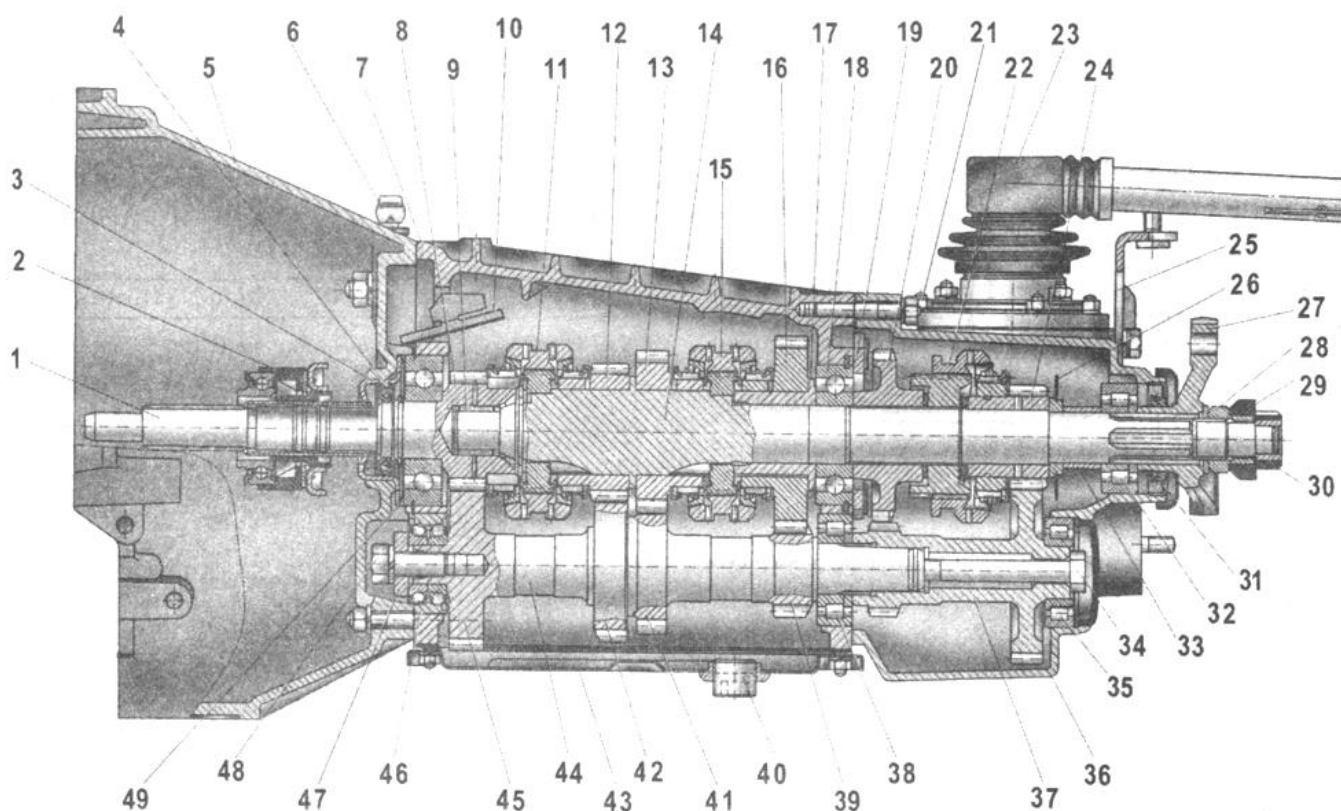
Коробка передач автомобиля Chevrolet «Niva»
